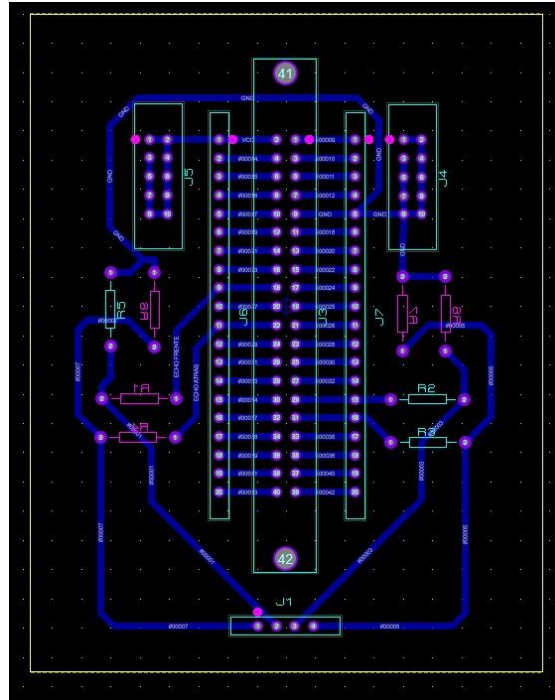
Diseño de la Placa PCB para la Conexión de los Sensores.
